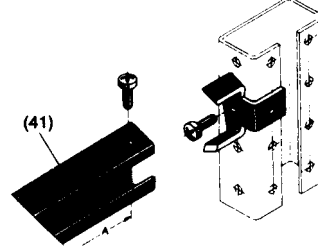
Kabelové připojovací soupravy pro max. 12 kabelů
